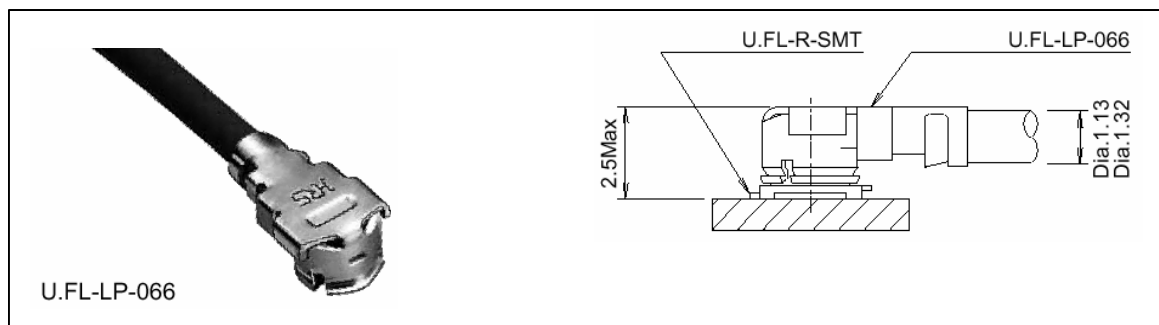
Разъем U.FL-R-SMT с вилкой U.FL-LP-066
